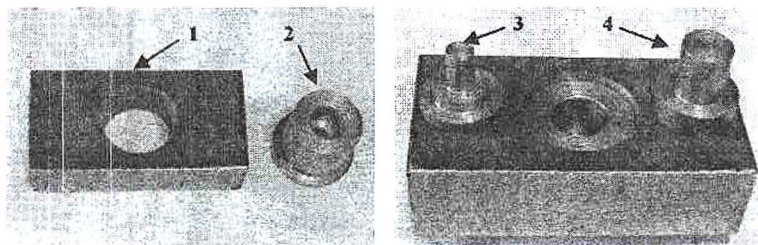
Инструмент для осадки с использованием магнитного поля: 1 – надставка; 2 – матрица; 3 – выталкиватель; 4 – пуансон
